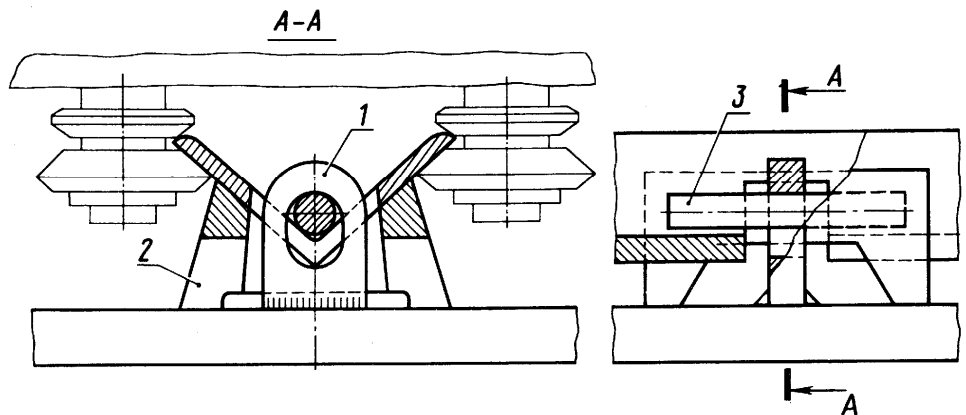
Крепление на изделии направляющего уголка сварочного автомата
